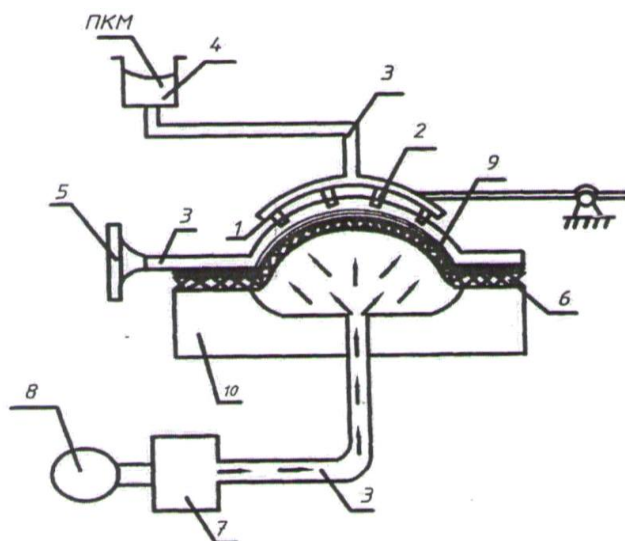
Вид А в сечении общего вида установки для формования объемных деталей одежды
